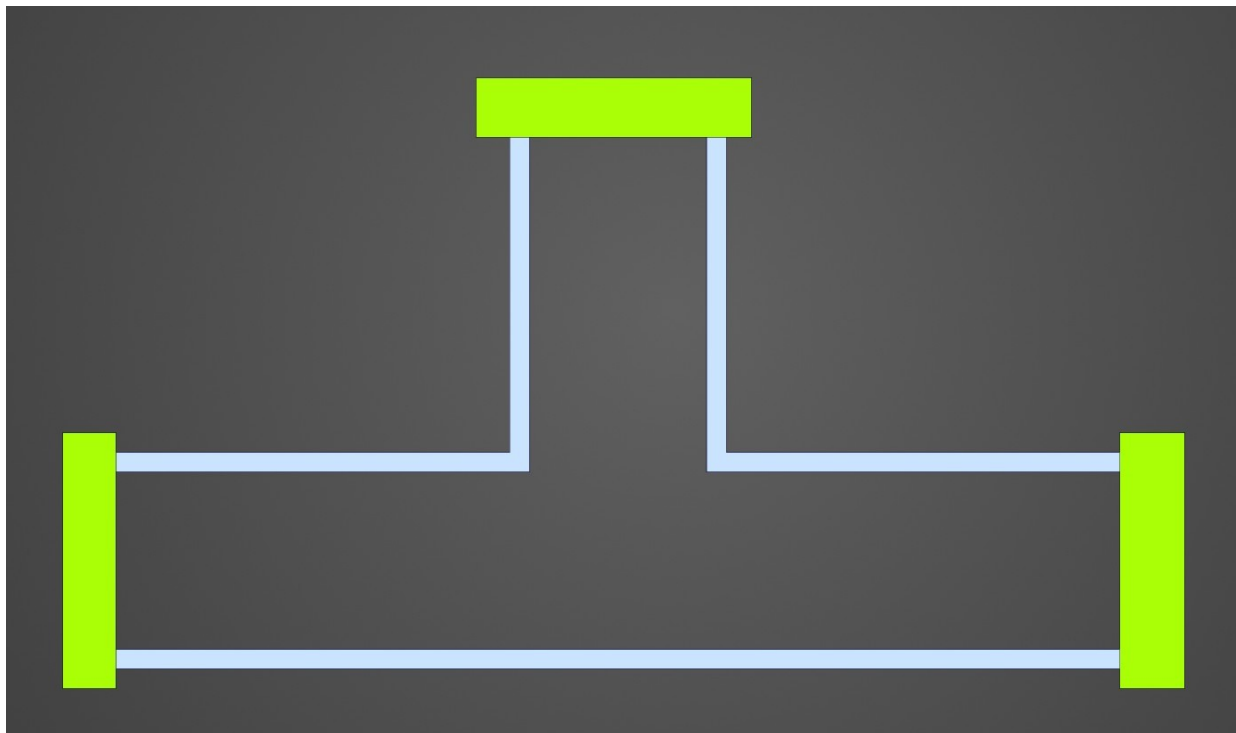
Кондуктор з 3 основними площинами закріплення (спеціальний зварний кондуктор)
